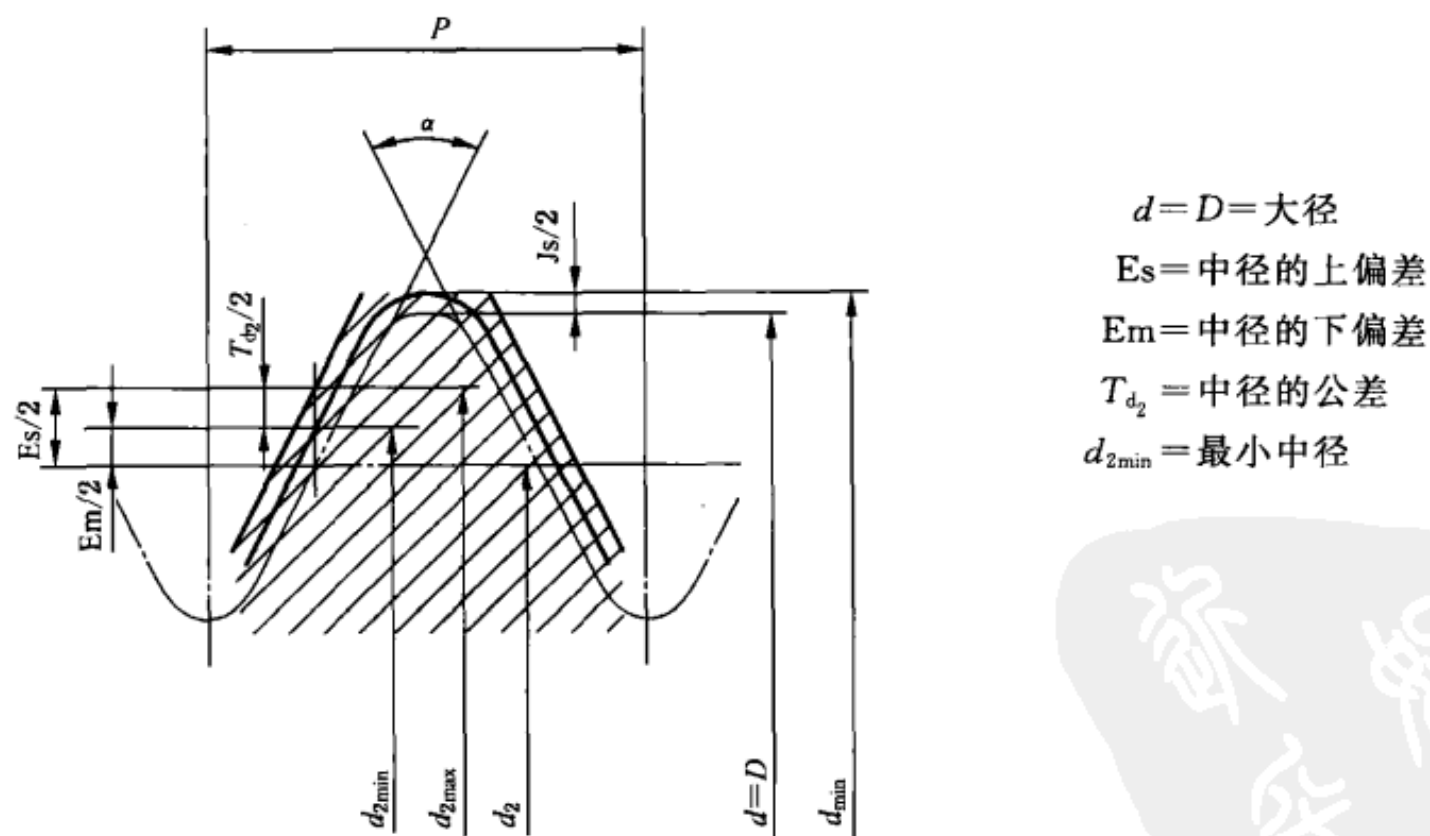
G 螺纹丝锥牙型和公差带位置
